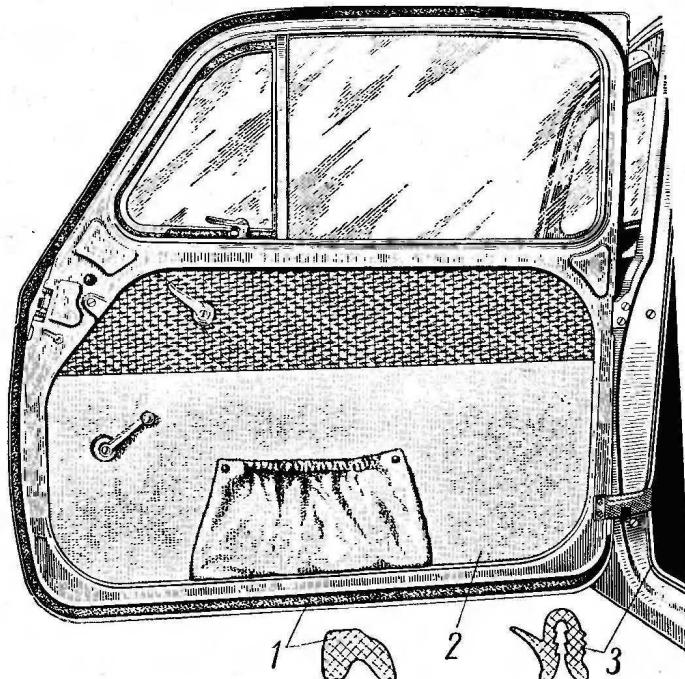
Tür mit Beschlägen, Fensterscheiben und Verkleidung, Türabdichtungen
